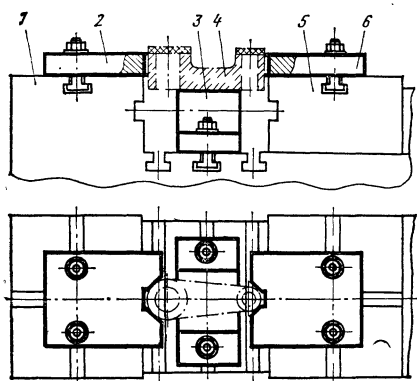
Наладка к универсальным наладочным тискам для закрепления деталей типа рычагов
